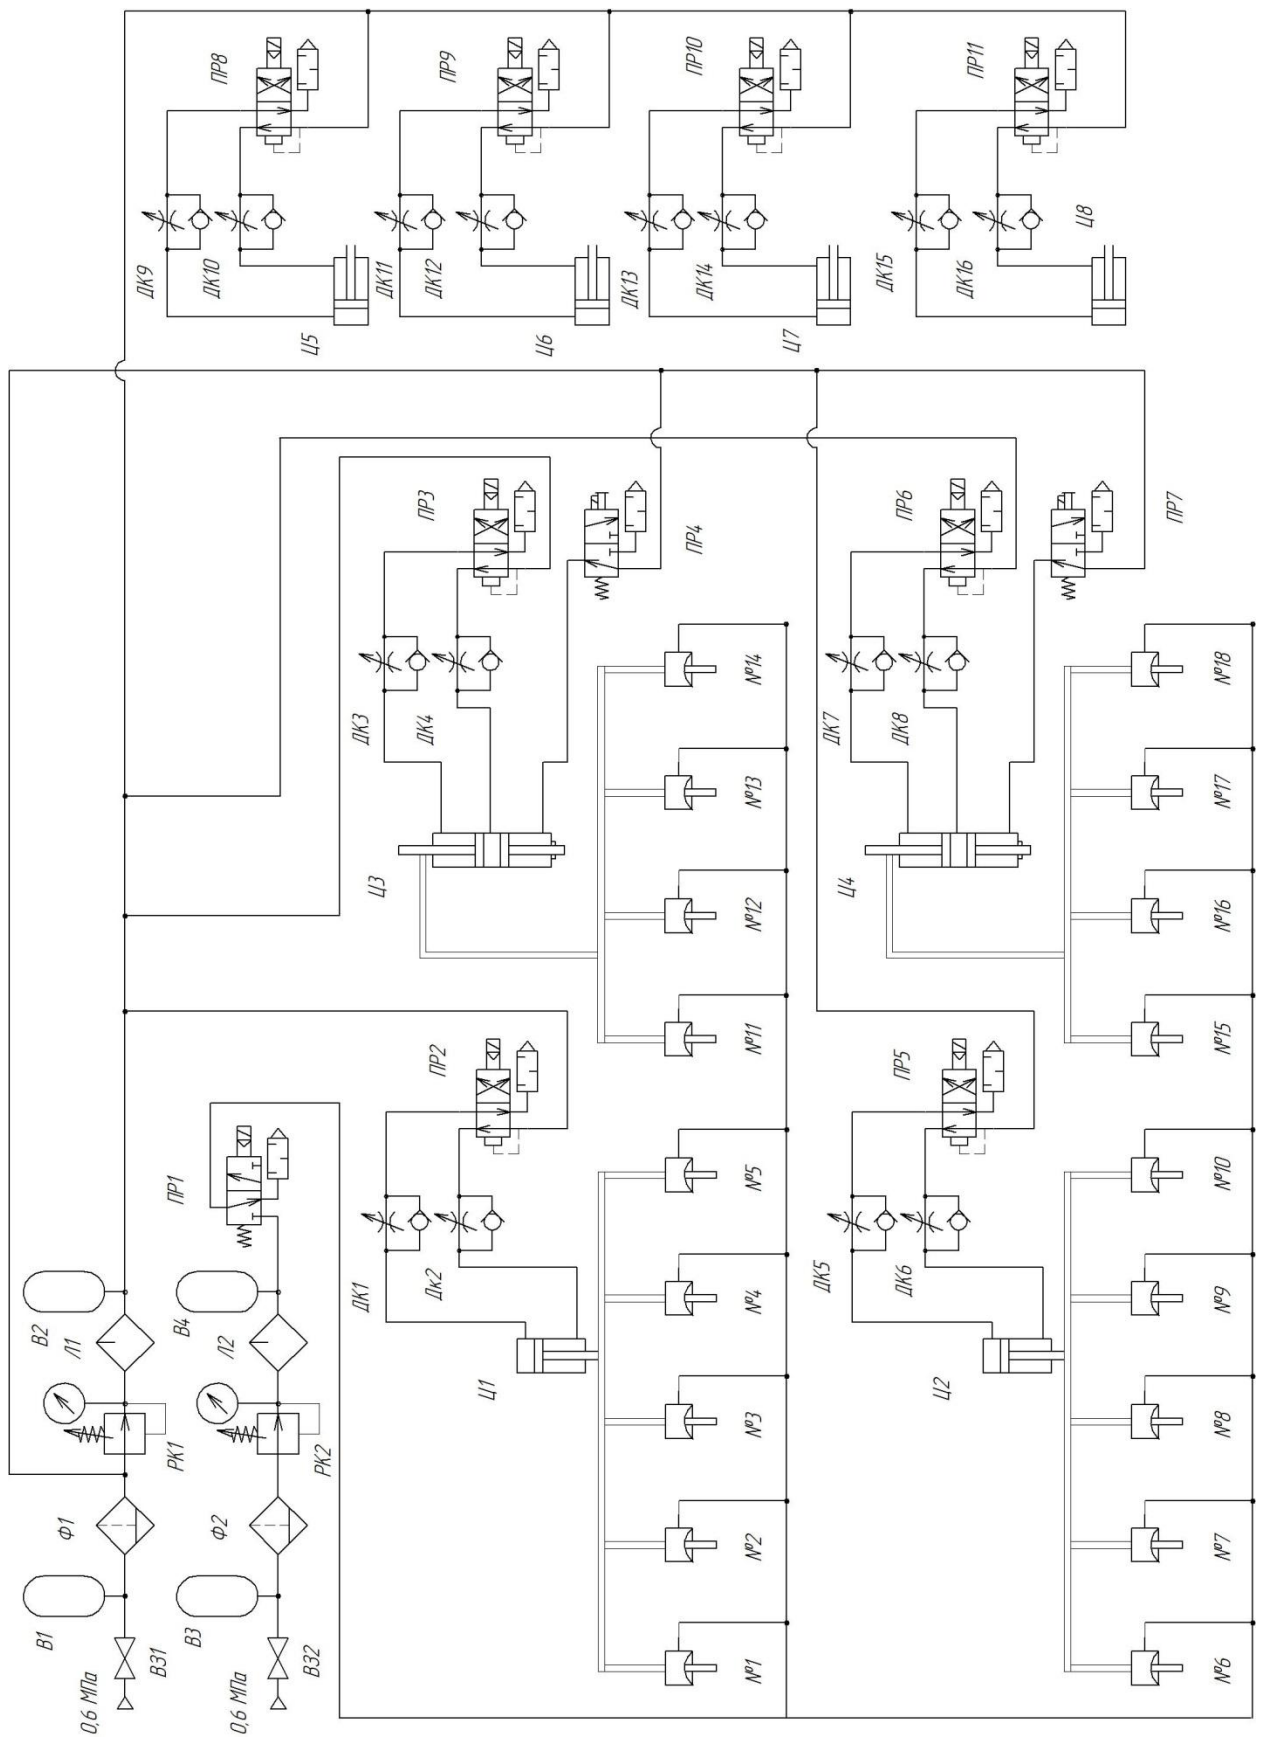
Пневматическая схема многоэлектродной сварочной машины
